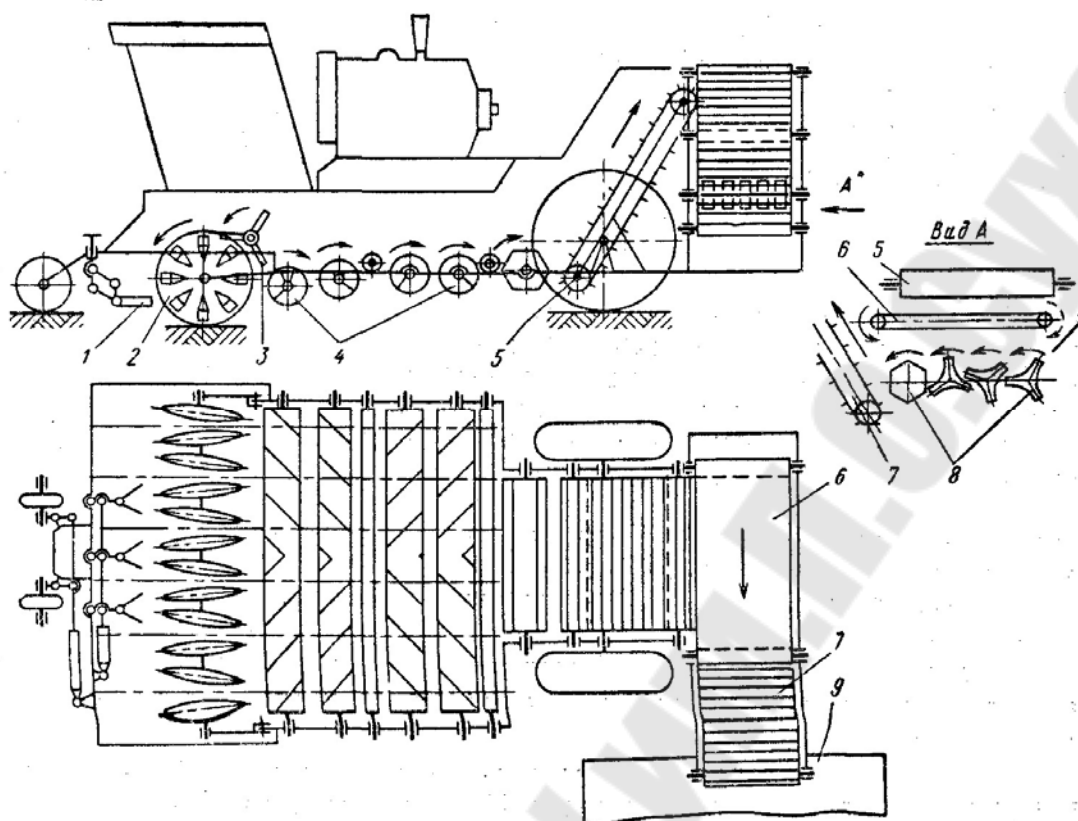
Схемакорнеуборочной машины КС-6
